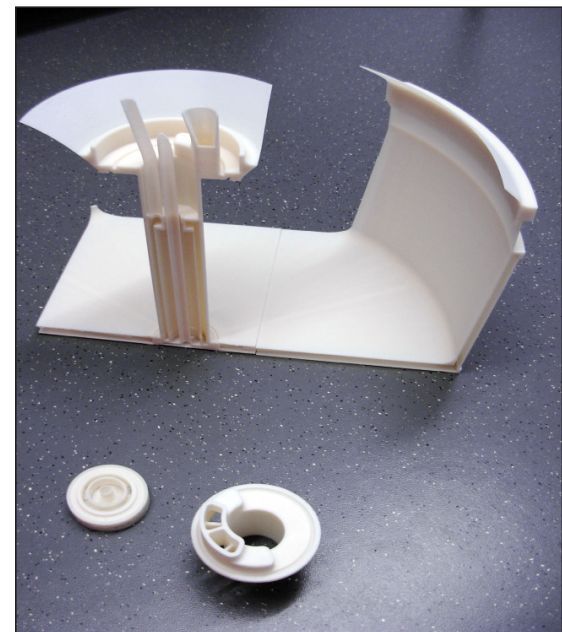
Design Review des Moderatorbehälters für das Projekt UCN.
